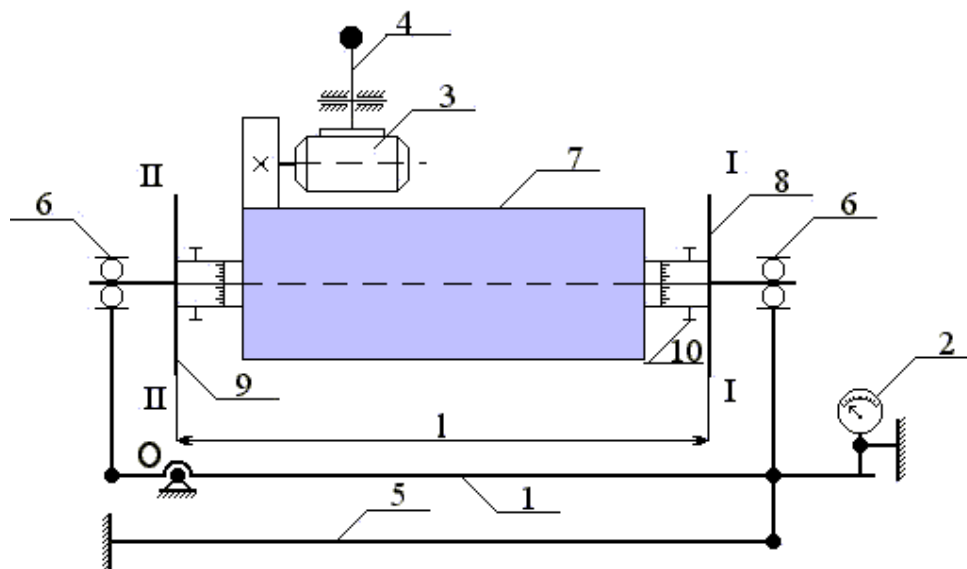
Схема станка для динамической балансировки ротора: 1-рама; 2 - индикатор; 3 - электромотор; 4 - рукоятка; 5 - торсионная пружина; 6 - подшипник; 7 - уравниваемый ротор; 8,9 - диски для установки уравнивающих масс; 10 - винт фиксации угловой координаты
